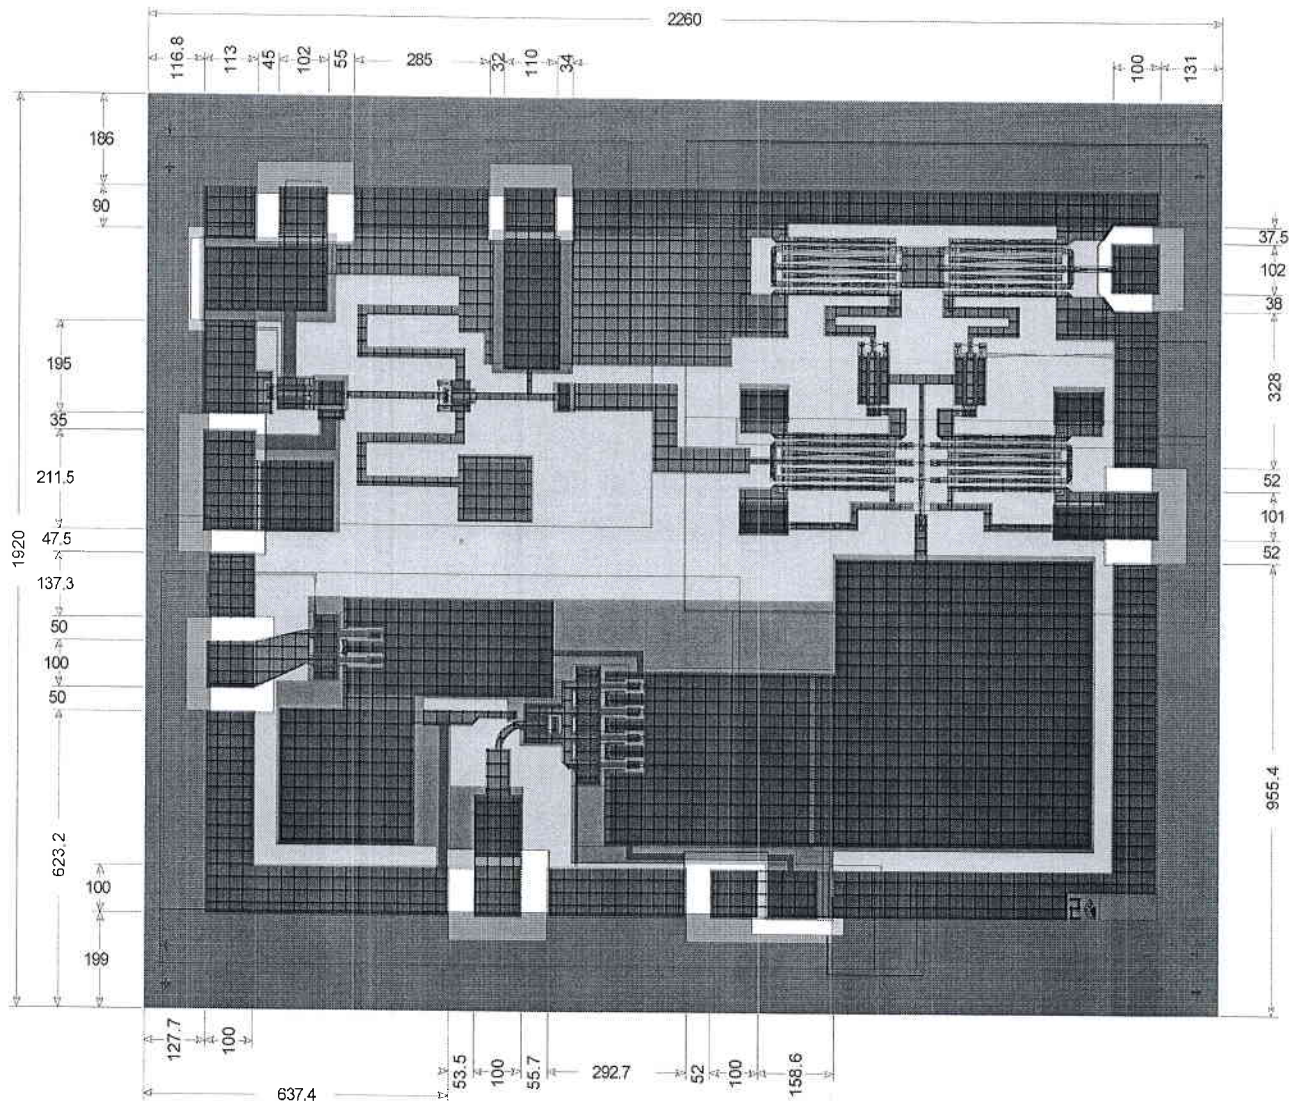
Габаритные чертежи МИС преобразователя сигнала
